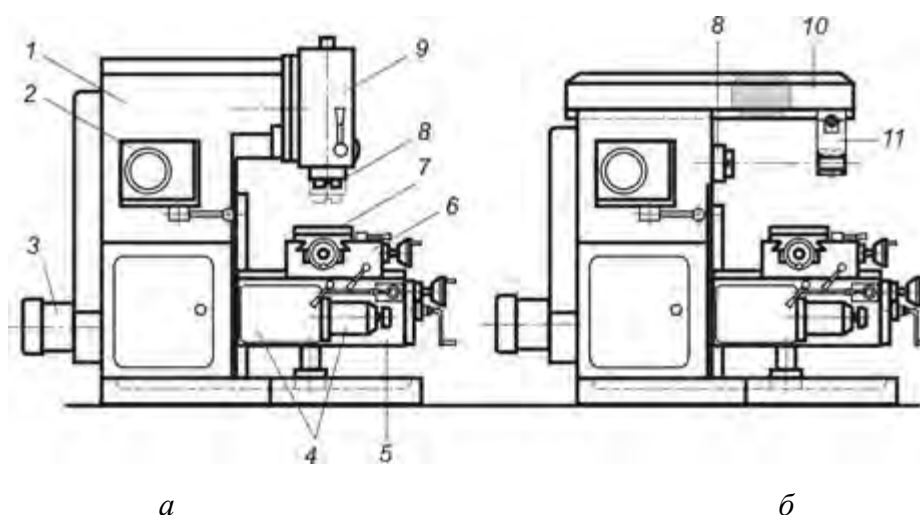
Схемы компоновок вертикально-фрезерного (а) и горизонтально-фрезерного (б) станков
